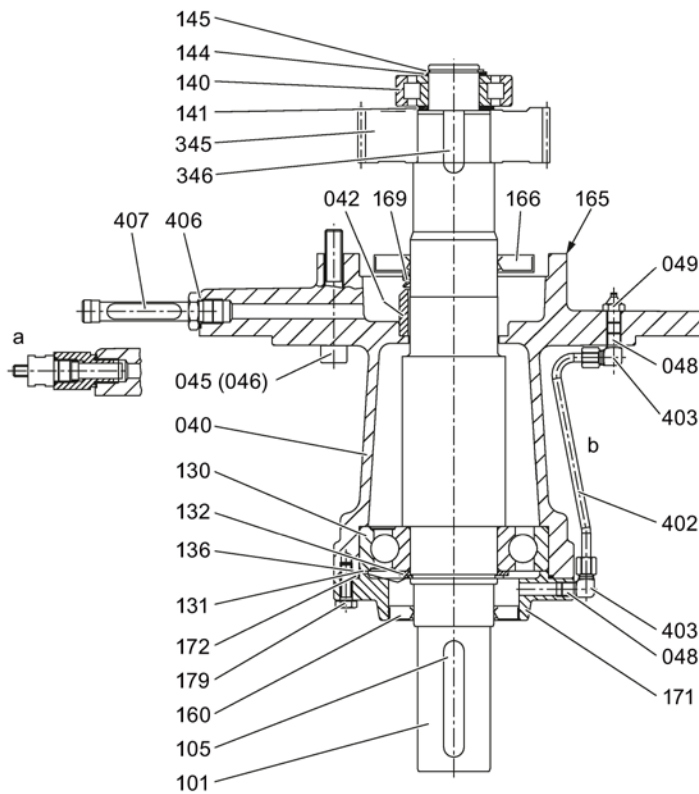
Rührwerksflansch Baugrößen 68 - 88
